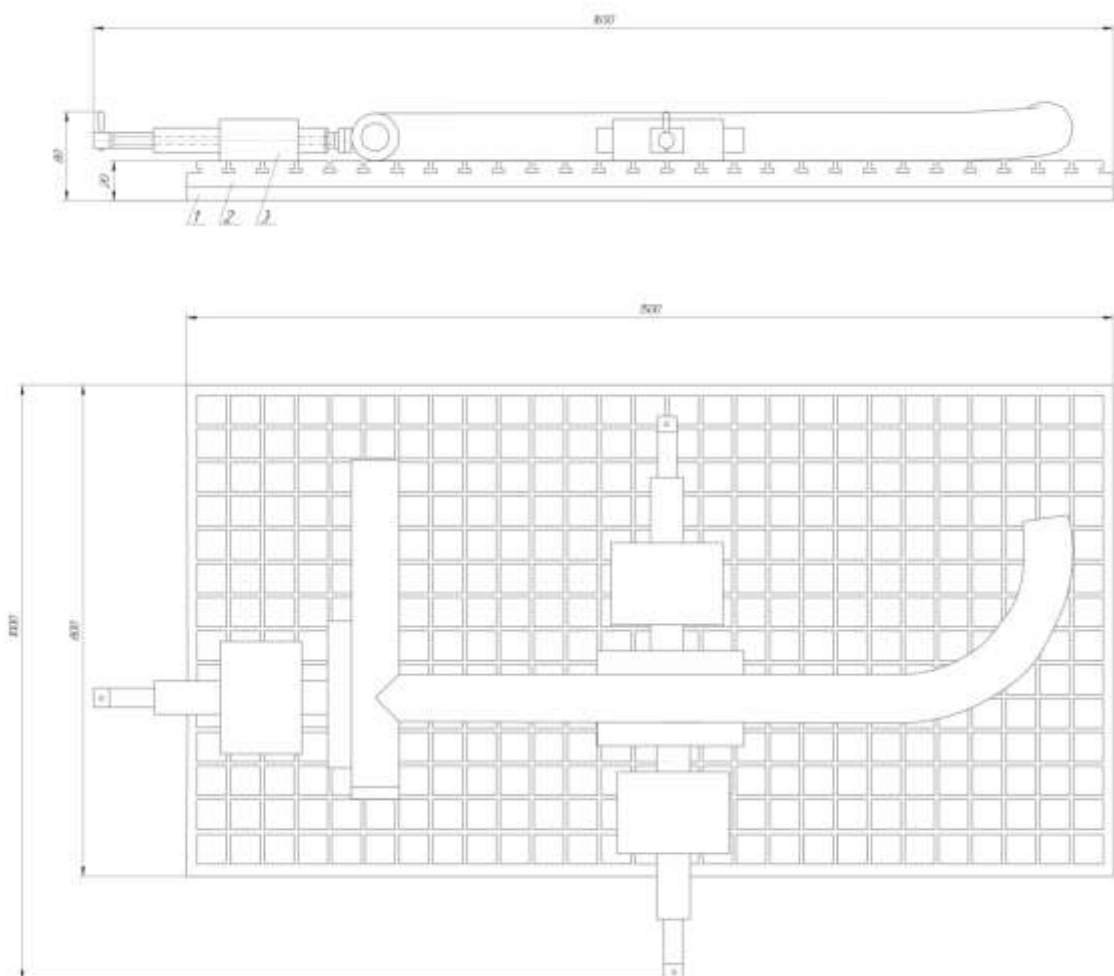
Загальний вигляд установки СРПЗ для зварювання калача доменної печі
